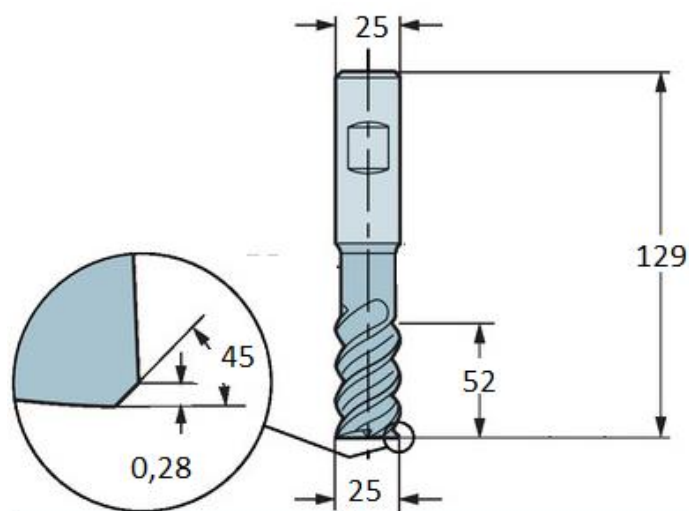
Концевая фреза Sandvik Coromant CoroMill 2P342-2500-PB 1730
